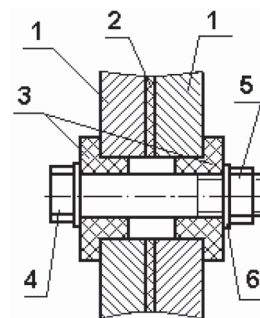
Сечение по крепежным деталям индуктора: 1 – шина; 2 – изоляционная пластина; 3 – изоляционная втулка; 4 – болт; 5 – гайка; 6 – шайба
